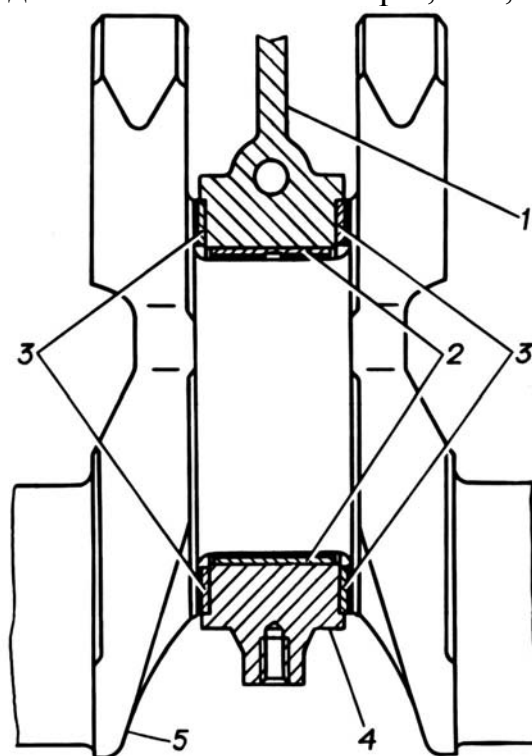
Средний (упорный) подшипник коленчатого вала: 1 - блок цилиндров; 2 - вкладыши подшипника; 3 - упорные полушайбы; 4 - крышка подшипника; 5 - коленчатый вал
